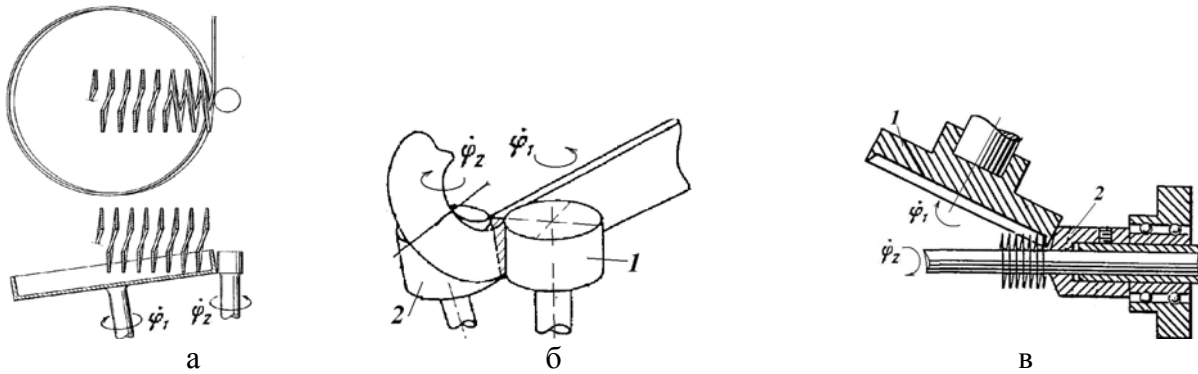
Схеми формоутворення ГЗ з робочими поверхнями інструментів у вигляді конусних та циліндричних поверхонь згідно патентів:
